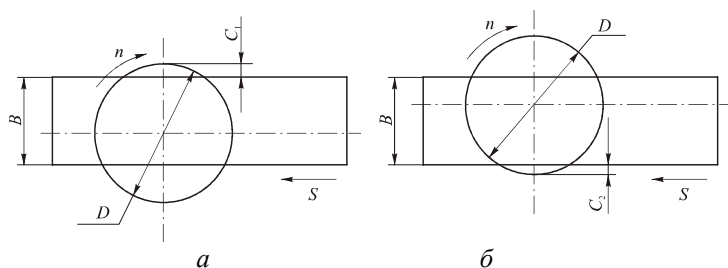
Расположение стальной заготовки при торцовом фрезеровании относительно фрезы: а – врезание зуба фрезы при $c_1 = (0,03 \dots 0,05) D$; б – выход зуба фрезы при $c_2 = 0$.
